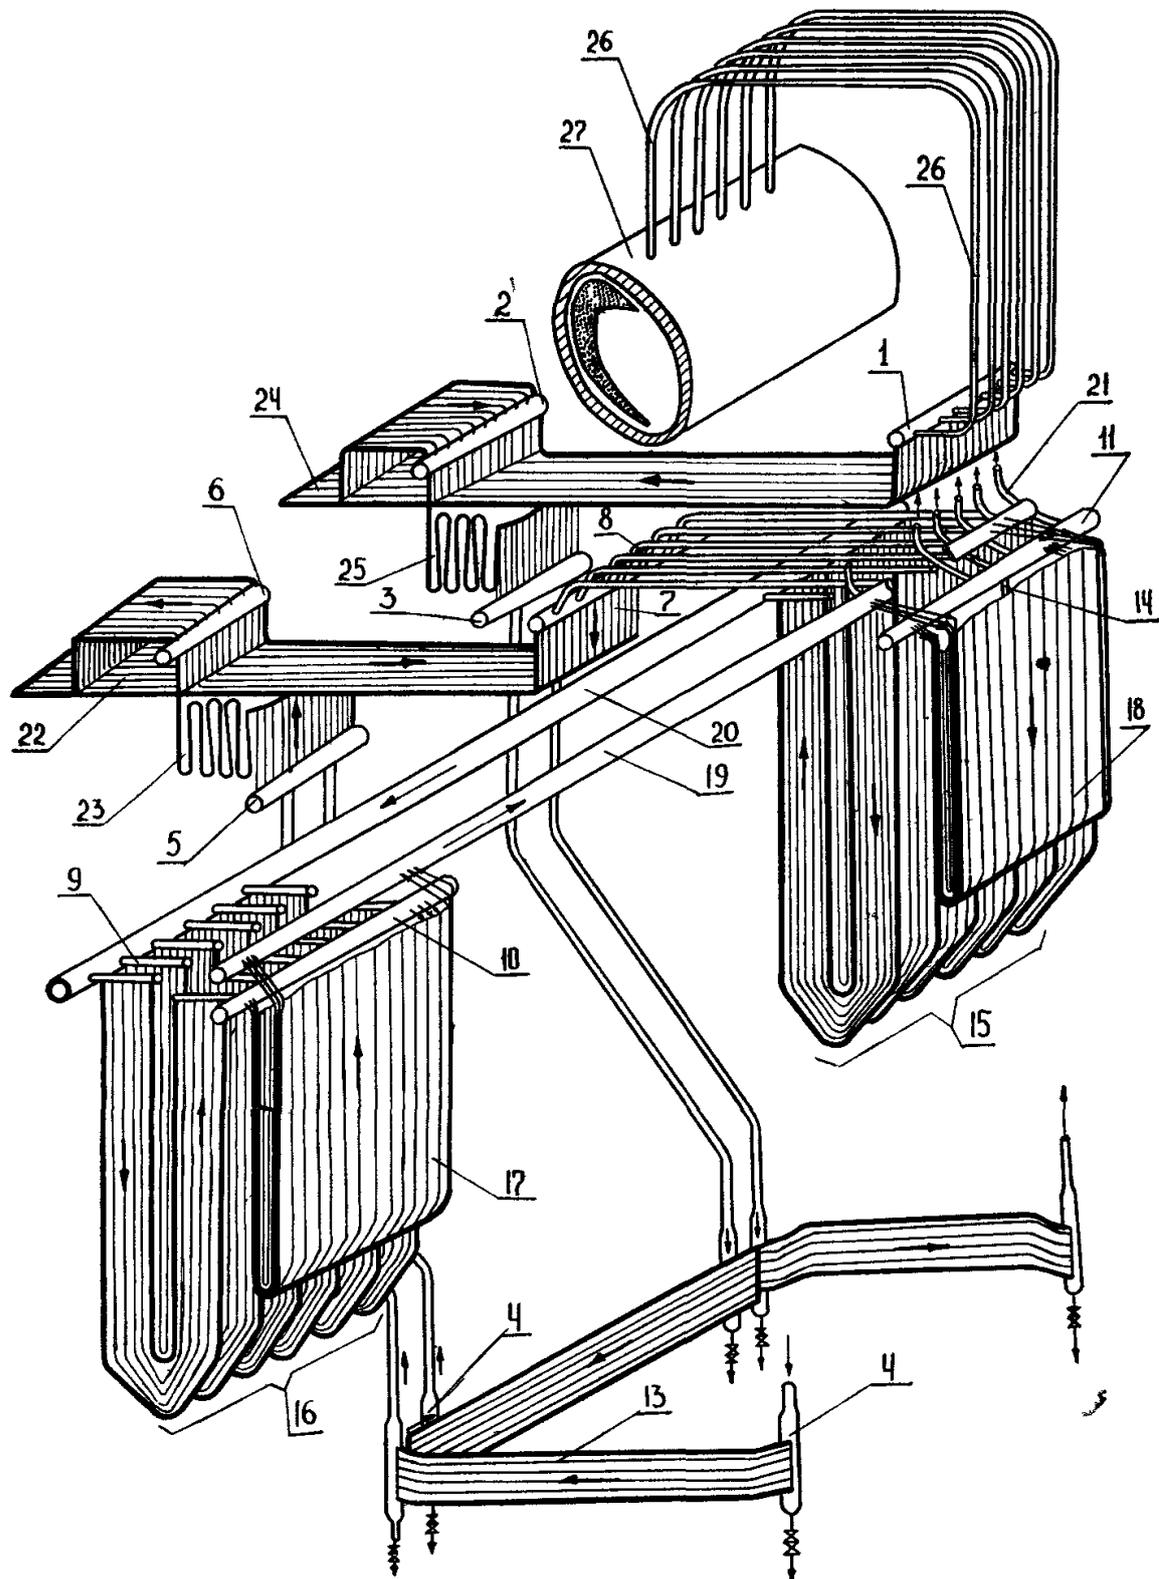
Компонка первичного пароперегревателя котла ТП 100
